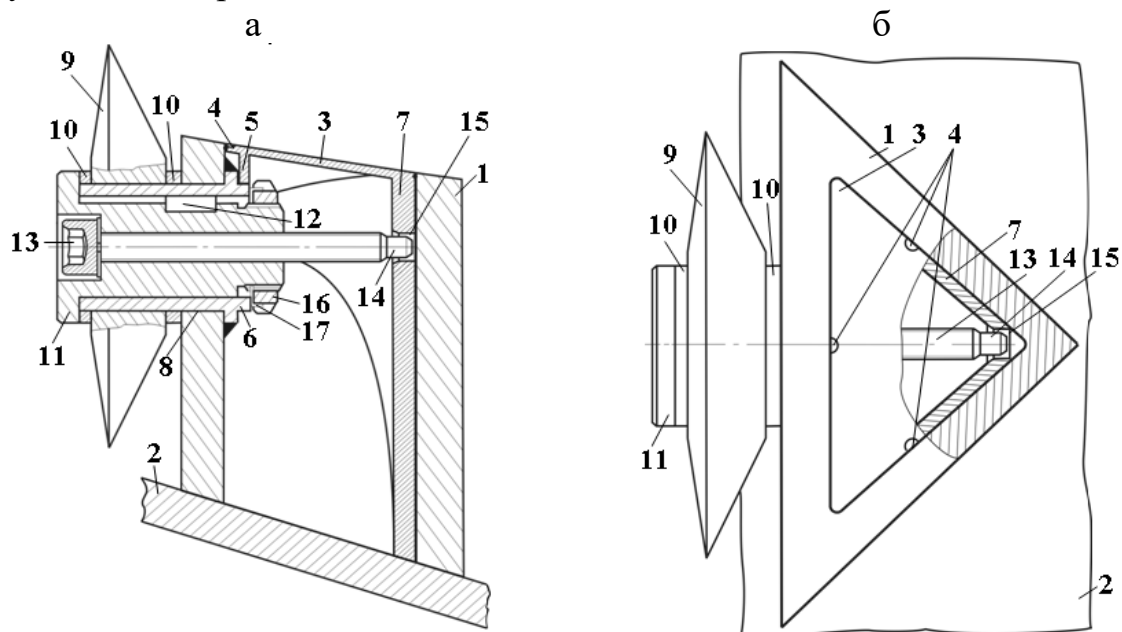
Конструкция узла совмещенного крепления дискового инструмента и крышки к трехгранной призме: а – внутренне пространство; б – вид сверху
